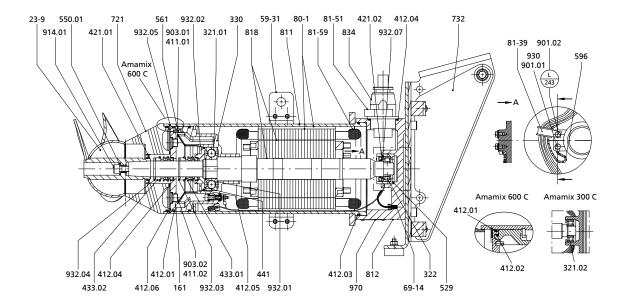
Чертеж общего вида Amamix 300/400/600, материал корпуса двигателя – высококачественная сталь
